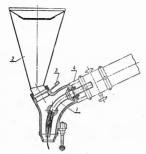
Держатель ДШ-5 шлангового полуавтомата ПШ-5:
